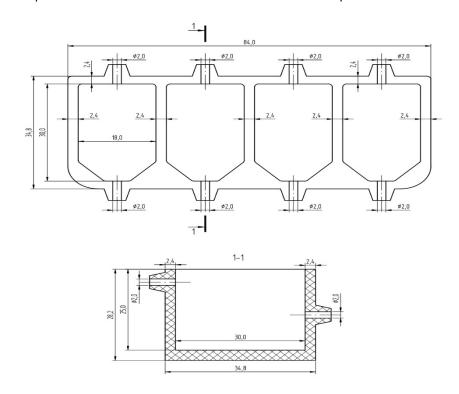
Чертеж блока с проточными ячейками (1). Вертикальный разрез проточной ячейки (1-1)
